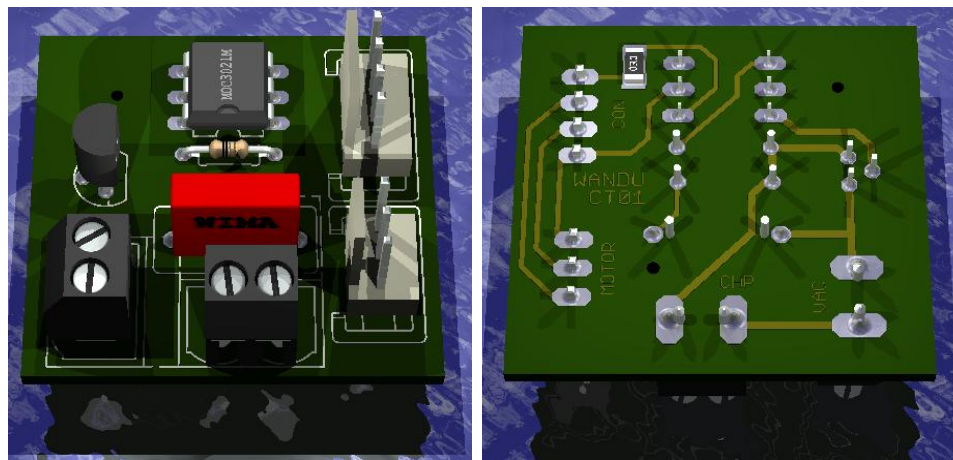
, PCB de la tarjeta de potencia del CT01 en 3D.
